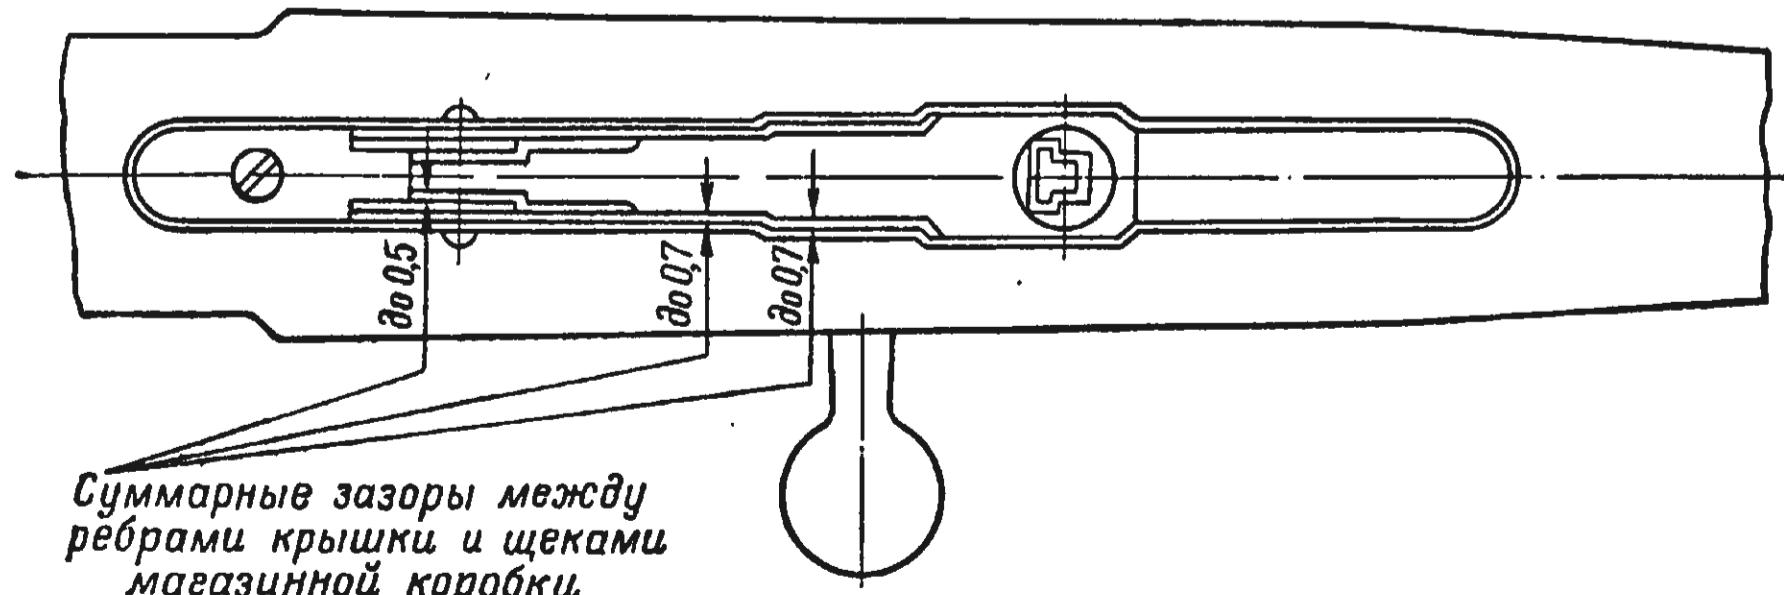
Допускаемые зазоры между щеками магазинной коробки и крышкой магазинной коробки
